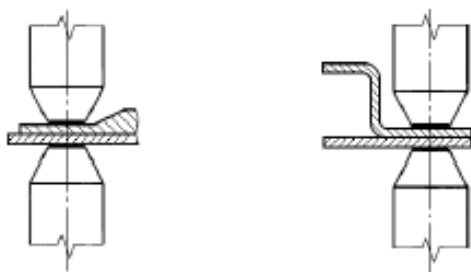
Eixo de soldadura perpendicular com chapa
